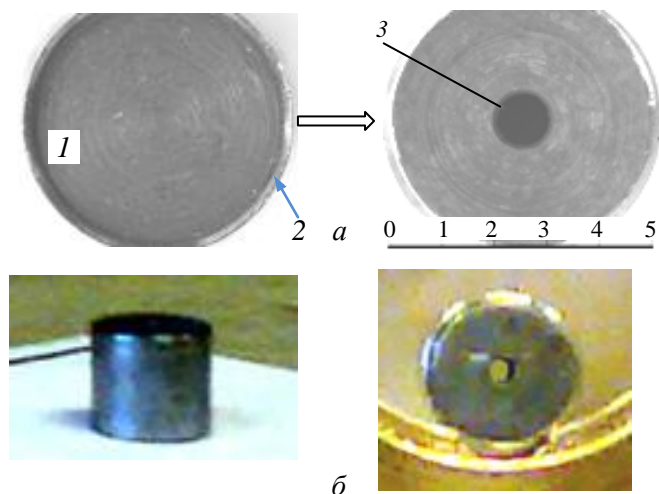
Свинцовая оболочка: а — формирование внутреннего цилиндрического отверстия: 1 — свинцовый цилиндр, 2 — прессформа (трубка из нержавеющей стали), 3 — цилиндрическое отверстие диаметром 1 мм; б — общий вид оболочки сбоку и с торца
